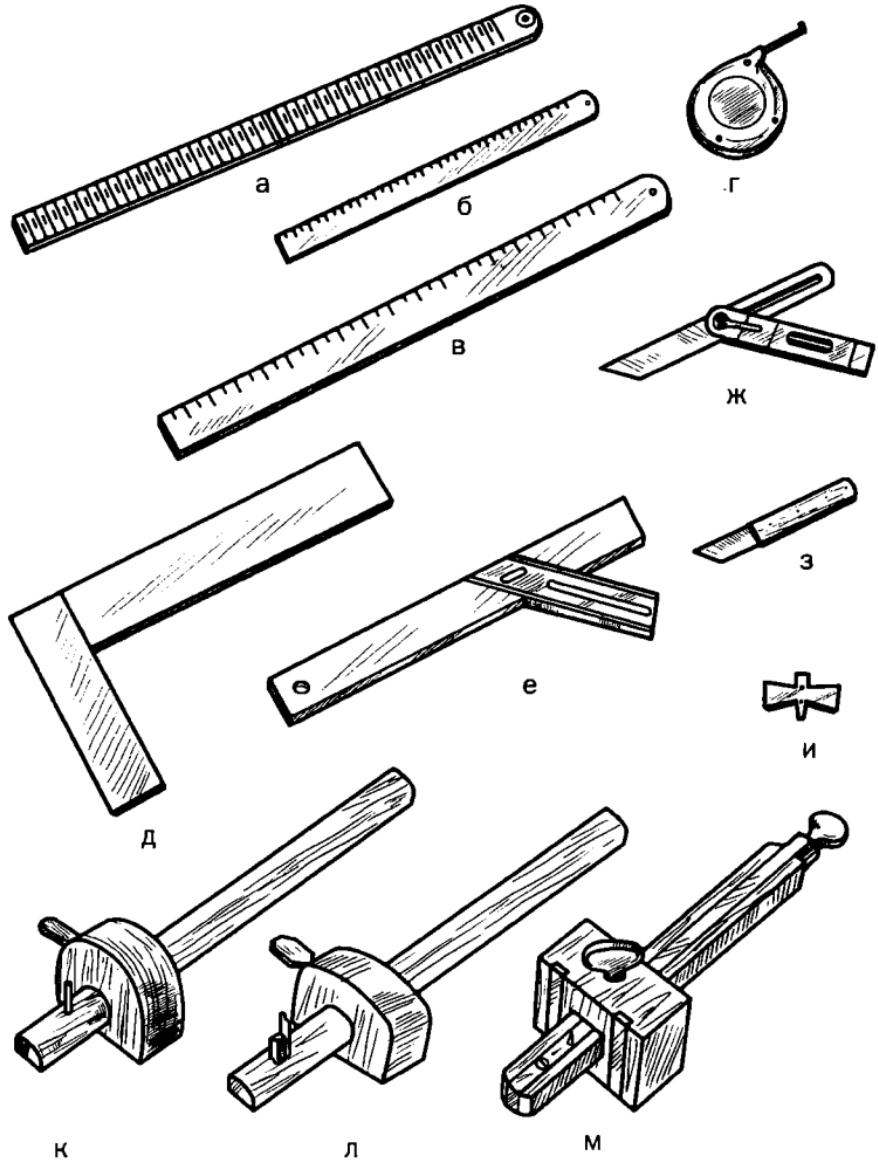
Измерительные и разметочные инструменты: а — складной метр; б — стальная линейка; в — поверочная линейка; г — рулетка; д — угольник; е — ерунок; ж — малка; з — разметочный нож; и — трафарет для соединения «ласточкин хвост»; к — разметочный рейсмус; л — режущий рейсмус; м — рейсмус для пазов
